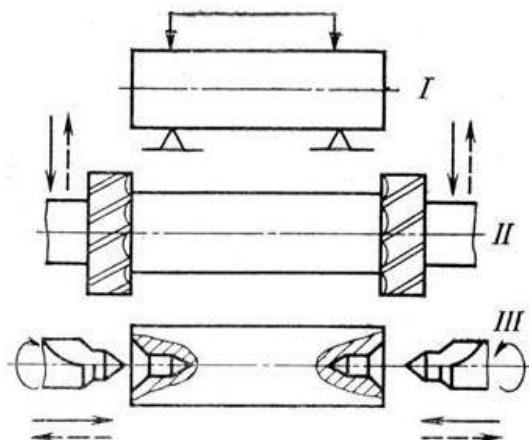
Схема обробки заготовки на фрезерно-центрувальному верстаті [3]
